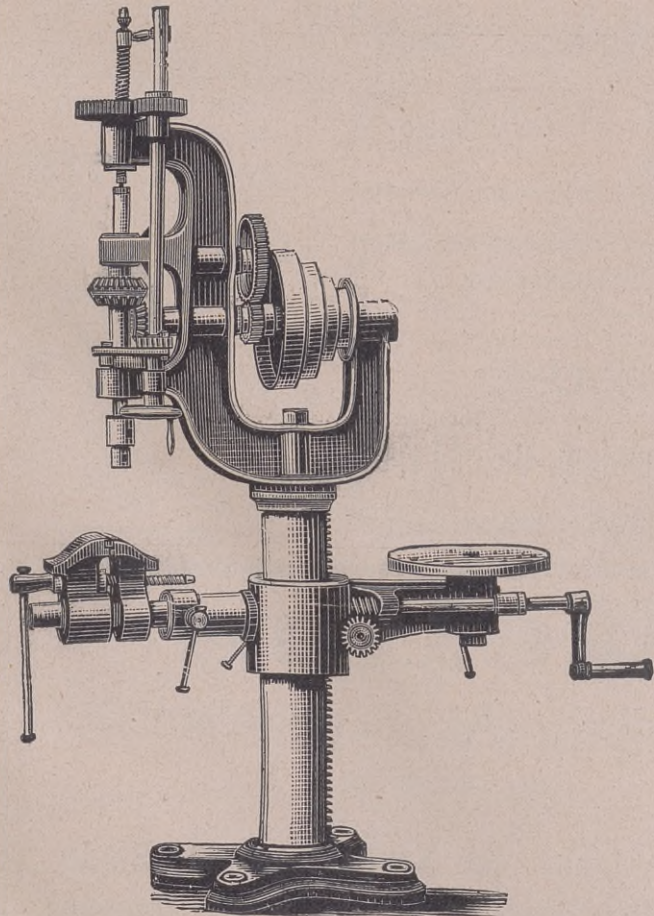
Säulenbohrmaschine für Kraftbetrieb.
